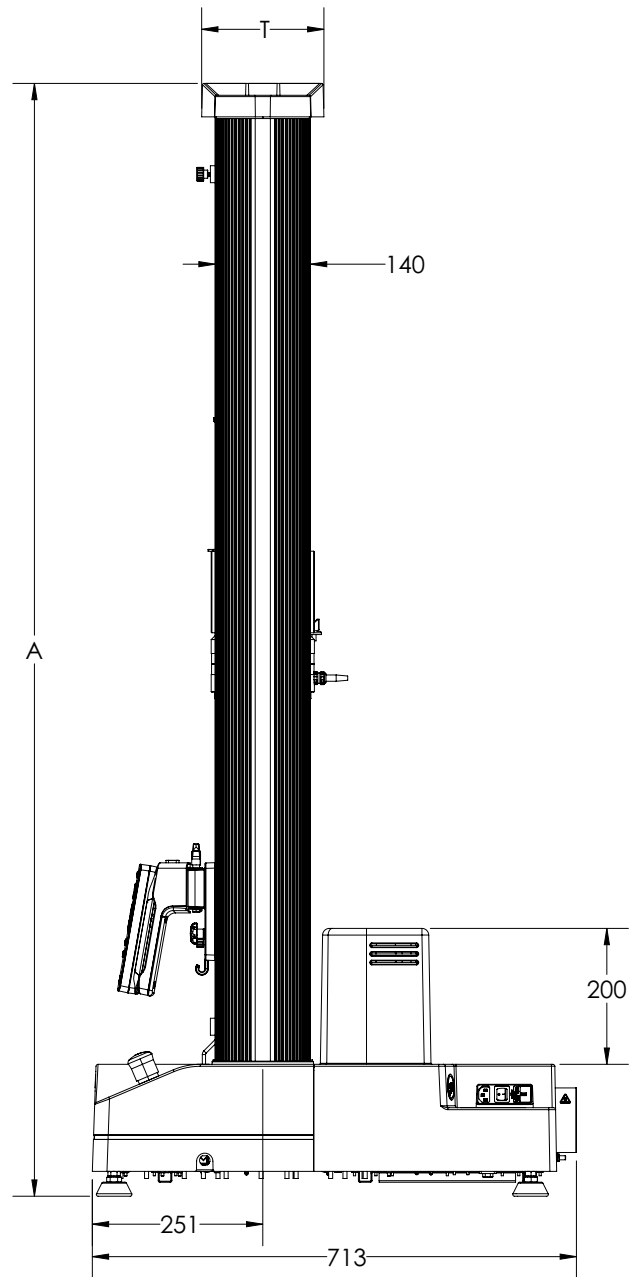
68TM-100 Prüfrahmabmessungen - Seitenansicht
